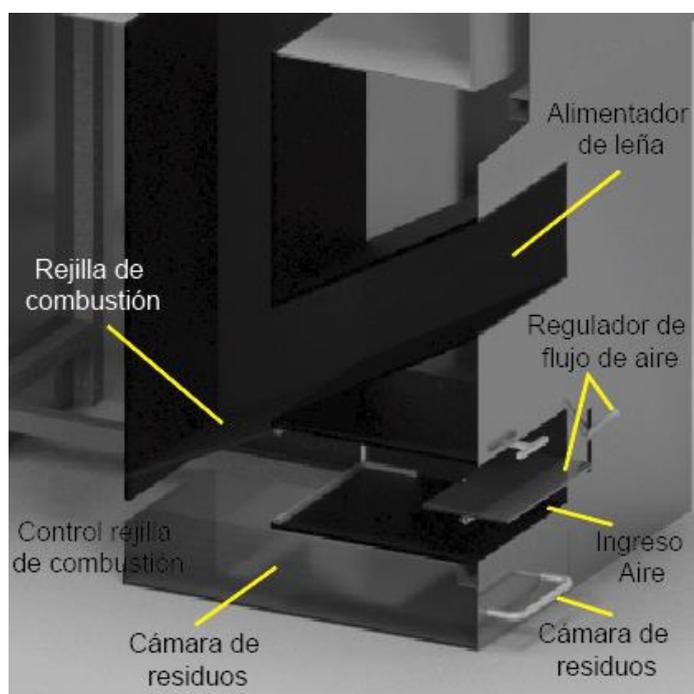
Corte transversal, detalle de alimentador de leña, aire, regulador de aire, rejilla de combustión & cajón de residuos.
